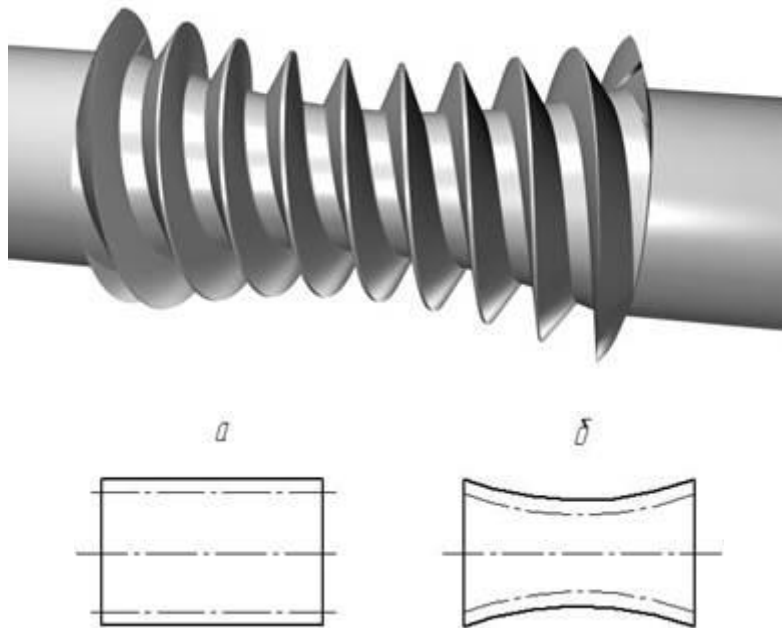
Схеми форм початкової поверхні черв'яка
